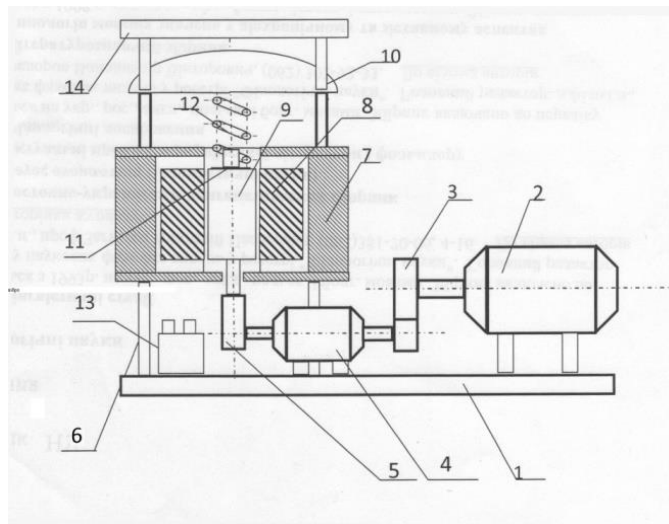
Схема пристрою для вібро-магнітно-абразивної обробки різальних пластин із ПКНБ
